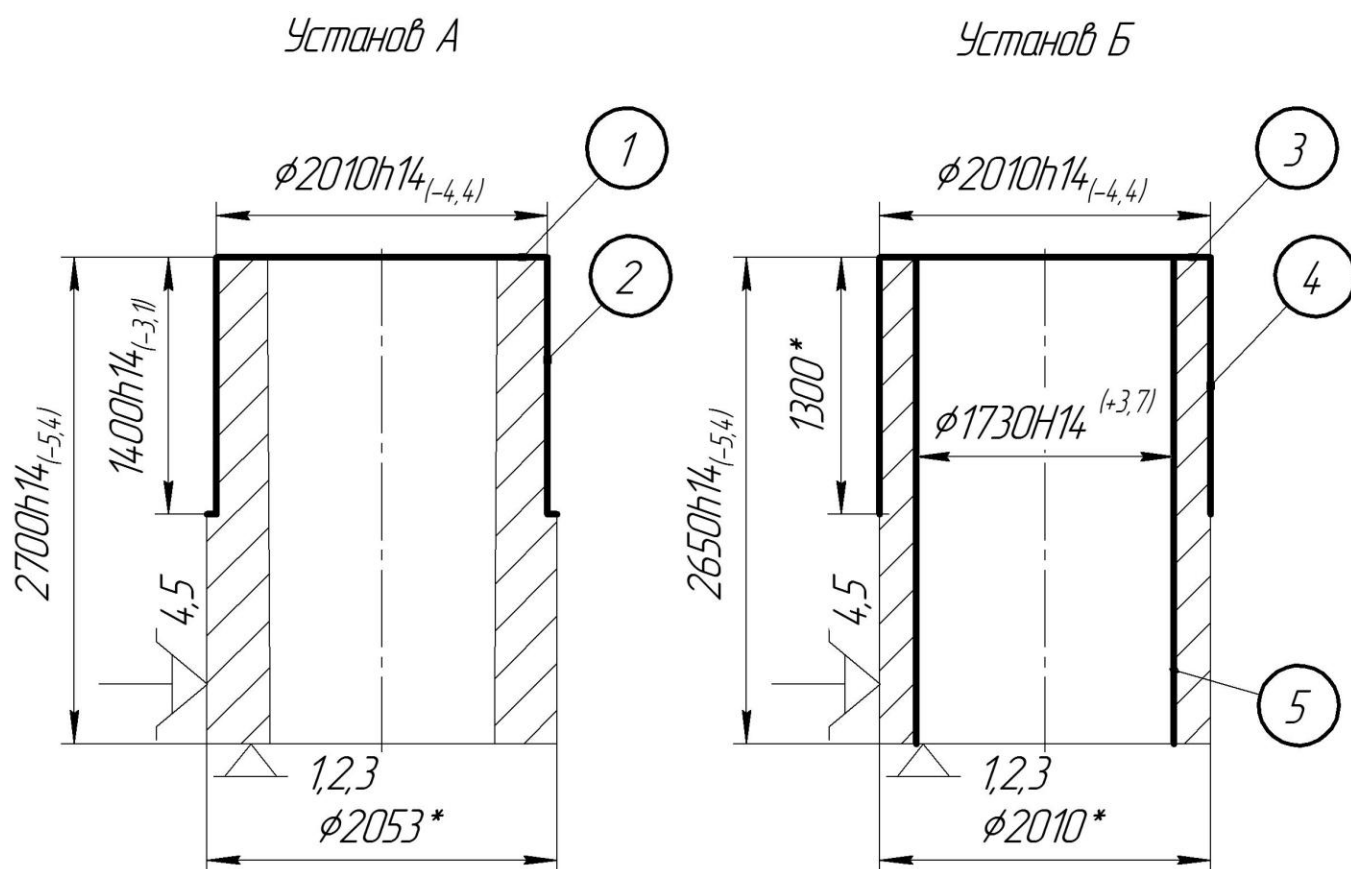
Схема базування заготовки на токарно-карусельній операції (перший варіант)
